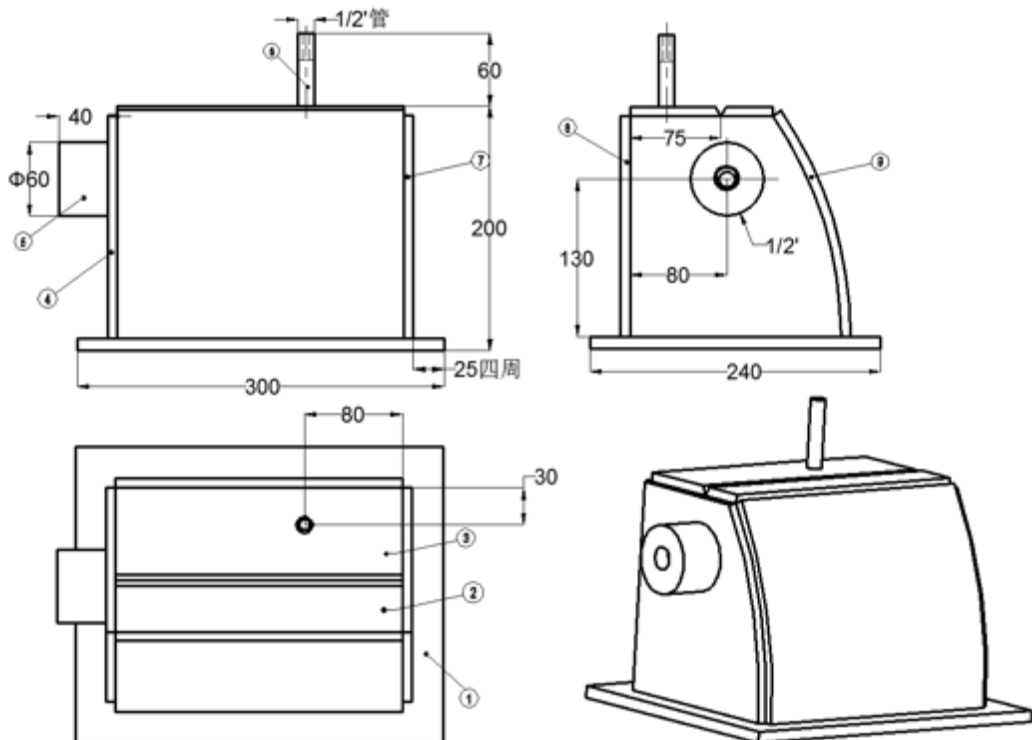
焊接机器人大赛实际操作竞赛试件图
